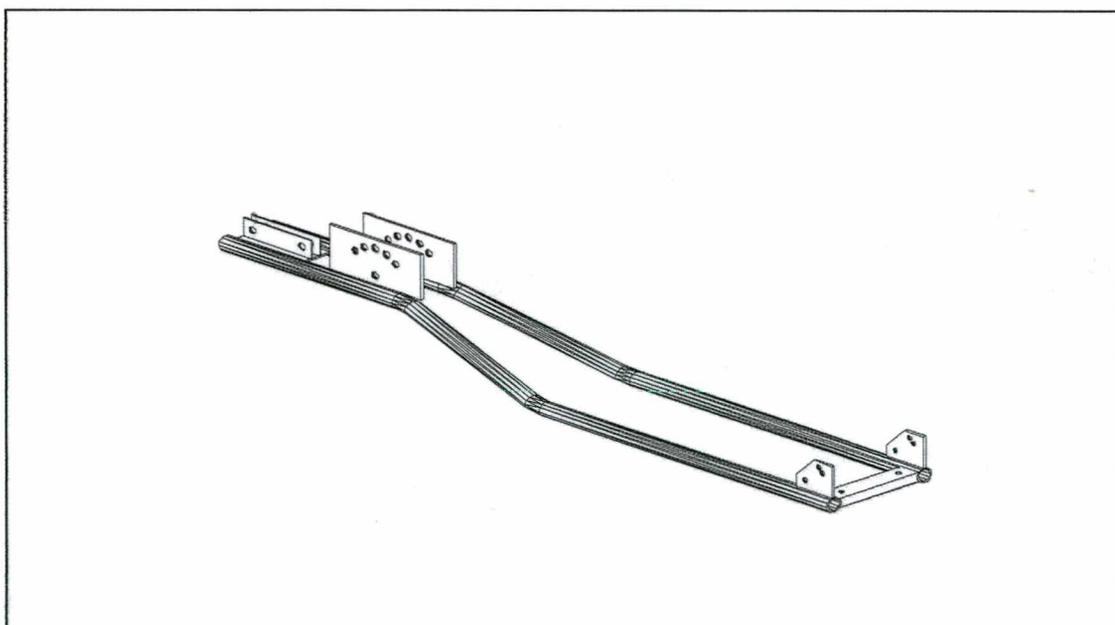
Desenho esquemático do Módulo Construtivo 12.
